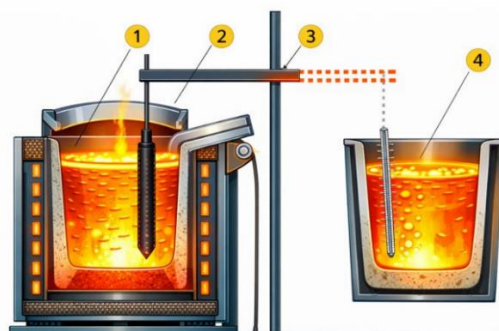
Схема индукционной печи и сталеразливочного ковша: 1 – индукционная печь; 2 – фурма; 3 – механизм поворота фурмы; 4 – сталеразливочный ковш
